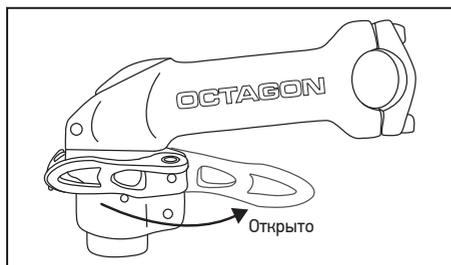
Установить рычаг быстроразъемного зажима в открытое положение
